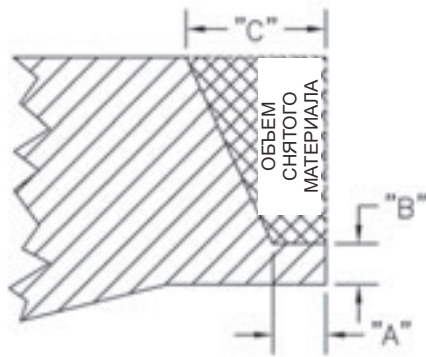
Формулы для расчета размеров фаски для профиля типа J-Prep.
